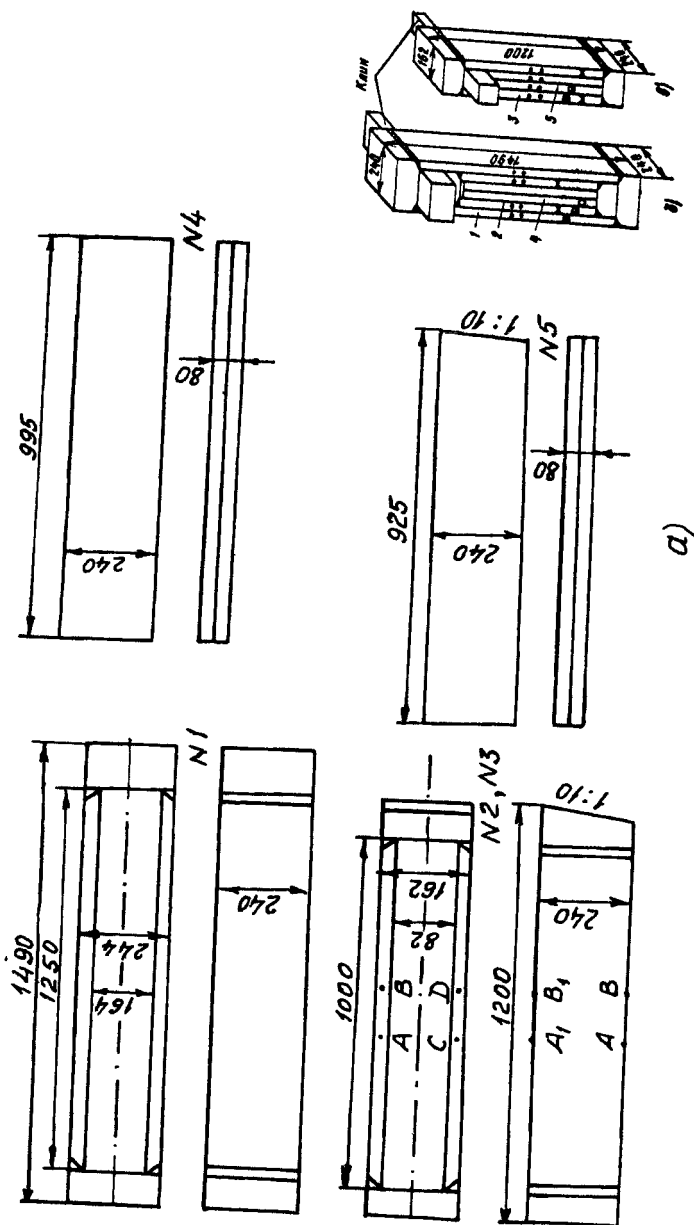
Образцы для исследования термомеханического воздействия на основной металл и сварные соединения
